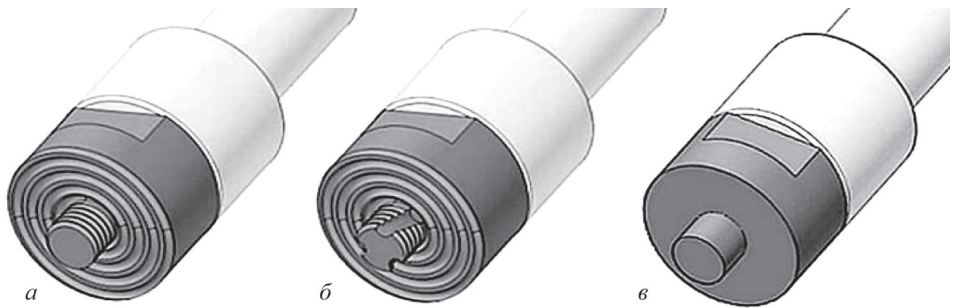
Инструменты для сварки трением с перемешиванием: а — тип С; б — Т; в — S
